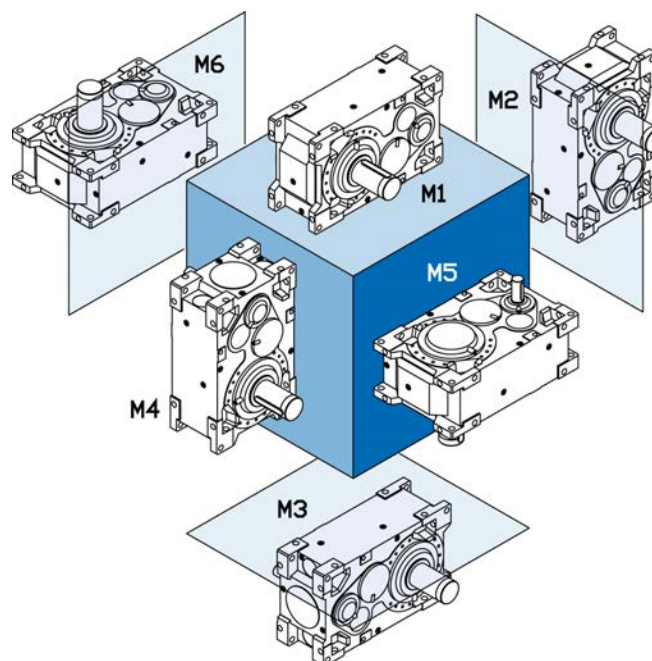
Монтажные положения цилиндрических соосных редукторов со стандартными монтажными поверхностями
